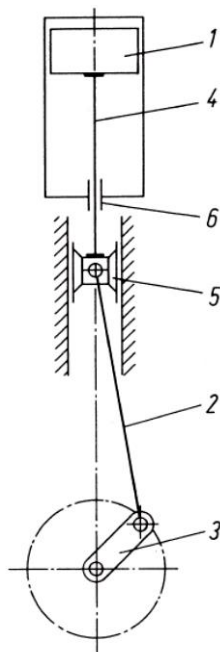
Skizze einer Hubkolbenmaschine;
